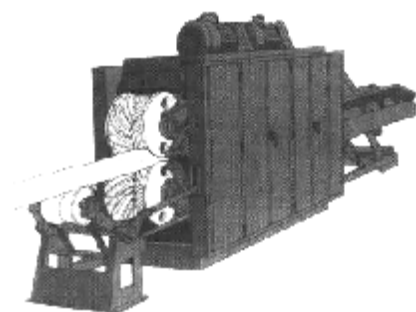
Общий вид окорочного станка ОК 63-2 Петрозаводского станкозавода
